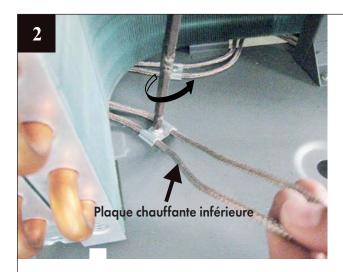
Remplacement du réchauffeur de la plaque inférieure – Unité extérieure
